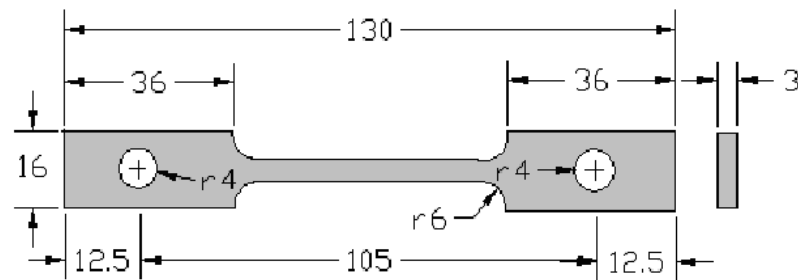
Geometria e dimensões do corpo de prova (unidade em mm)
